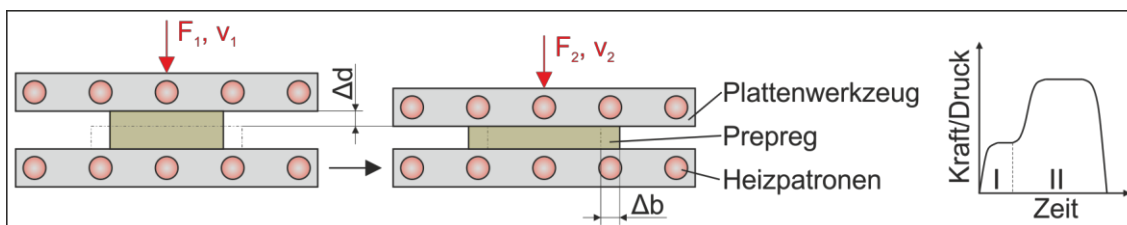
Versuchsaufbau für die offenen Werkzeuge
